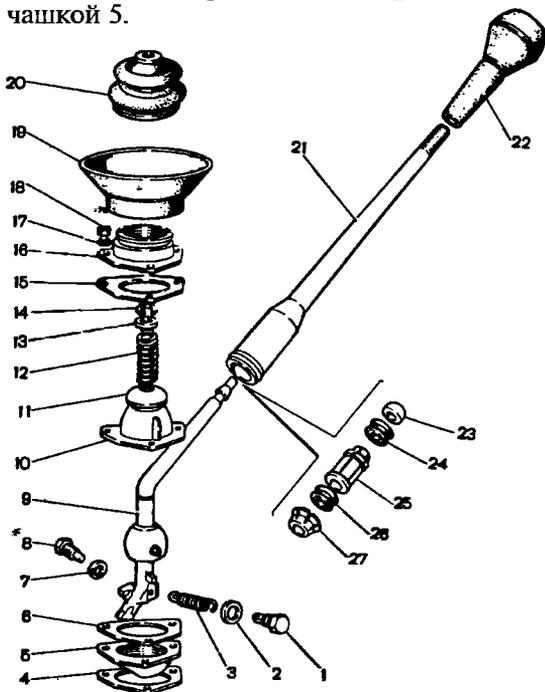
Детали рычага переключения передач: 1 - болт оттяжной пружины; 2 - шайба; 3 - оттяжная пружина; 4 - прокладка; 5 - направляющая чашка; 6 - прокладка; 7 - шайба; 8 - ограничительный болт; 9 - рычаг переключения передач; 10 - шаровая опора; 11 - сферическая шайба; 12 - пружина; 13 - опорная шайба; 14 - стопорное кольцо; 15 - прокладка; 16 - фланец; 17 - пружинная шайба; 18 - гайка; 19 - манжета; 20 - внутренний чехол; 21 - стержень рычага; 22 - рукоятка; 23 - упорная подушка; 24 - упругая втулка; 25 - дистанционная втулка; 26 - упругая втулка; 27 - запорная втулка
